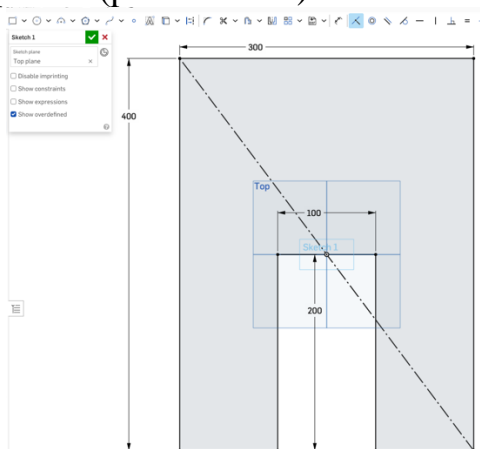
а. Креслення основи деталі (sketch), яка розглядається в задачі.
